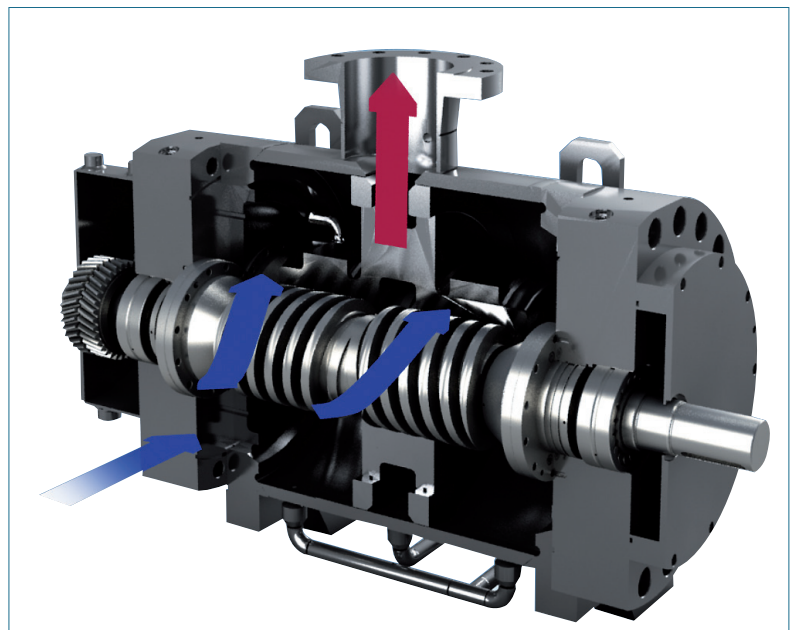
Innenansicht einer Hochdruck-Multiphasenpumpe
